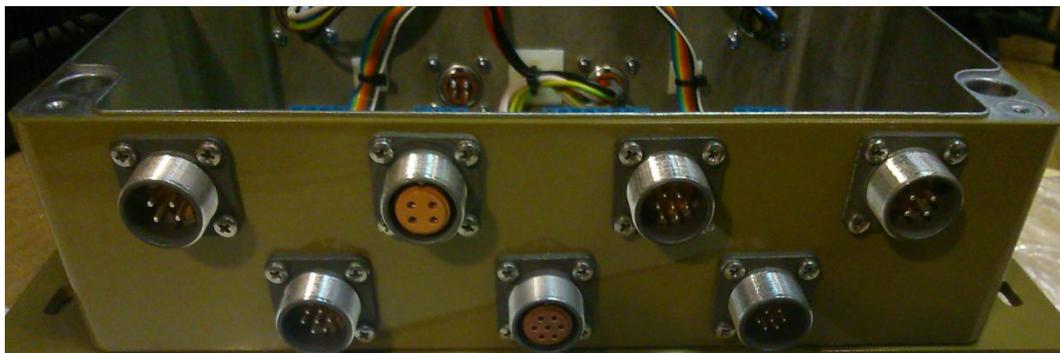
Внешний вид левой боковой стенки БУА 1200
